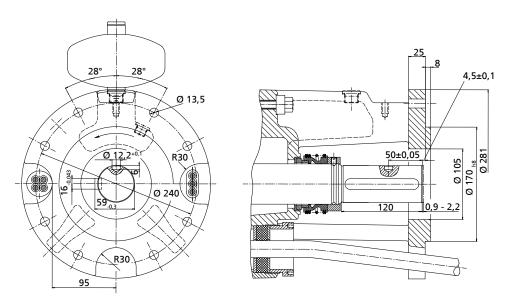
Dimensiones de conexión de UMA 300, 4 polos, dimensiones indicadas en [mm]
